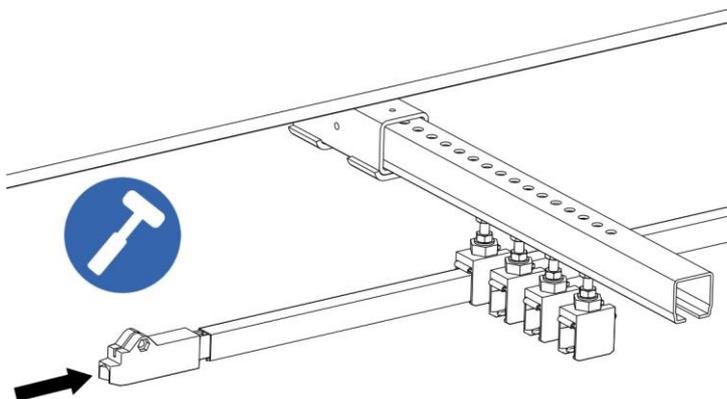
Pousser l'embout final sur l'extrémité du rail conducteur
